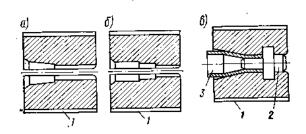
Схема штампового инструмента радиально-ковочной машины для ковки одноступенчатых (а) и многоступенчатых (б) валов и трубных заготовок на оправке (в): 1 – бойки; 2 – оправка; 3 – поковка
